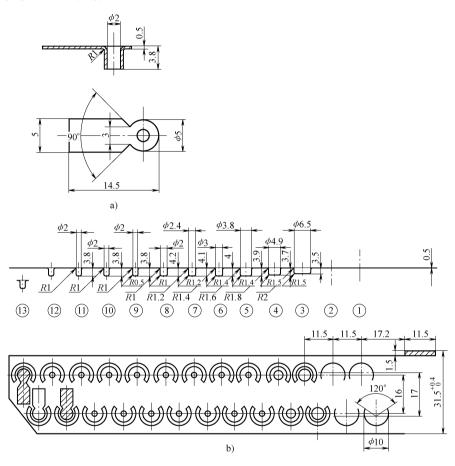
焊片 a) 零件图 b) 排样图
